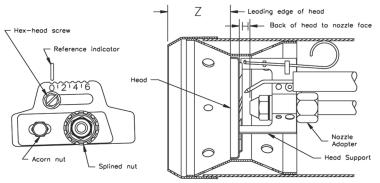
Réglage de la dimension « Z » de Beckett AFG - régulateurs V1
